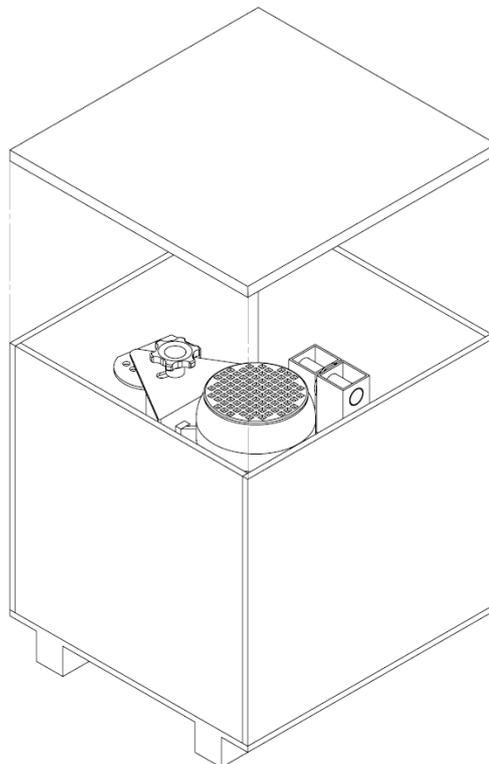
Retirando tampa superior da caixa de embalagem do ventilador
